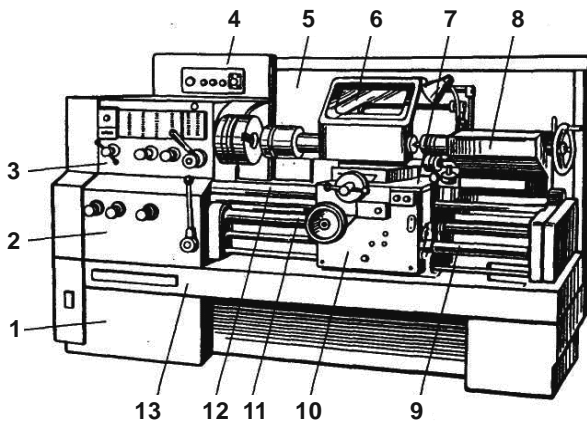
Токарно-гвинторізний верстат: 1 – основа верстата; 2 – коробка передач; 3 – передня бабка; 4 – електрична шафа; 5 – екран; 6 – щиток; 7 – супорт; 8 – задня бабка; 9 – ходовий вал; 10 – фартух; 11 – ходовий гвинт; 12 – станина; 13 – корито для збирання стружки
